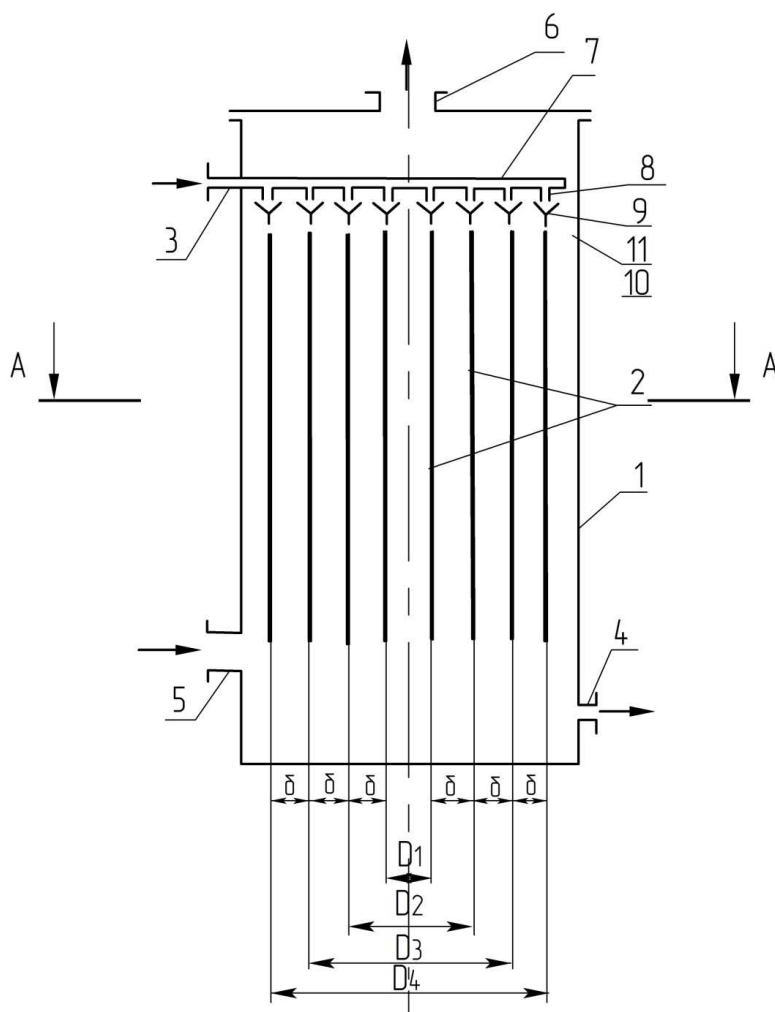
Общий вид в разрезе колонны с трубчатыми рукавами предлагаемой конструкции
